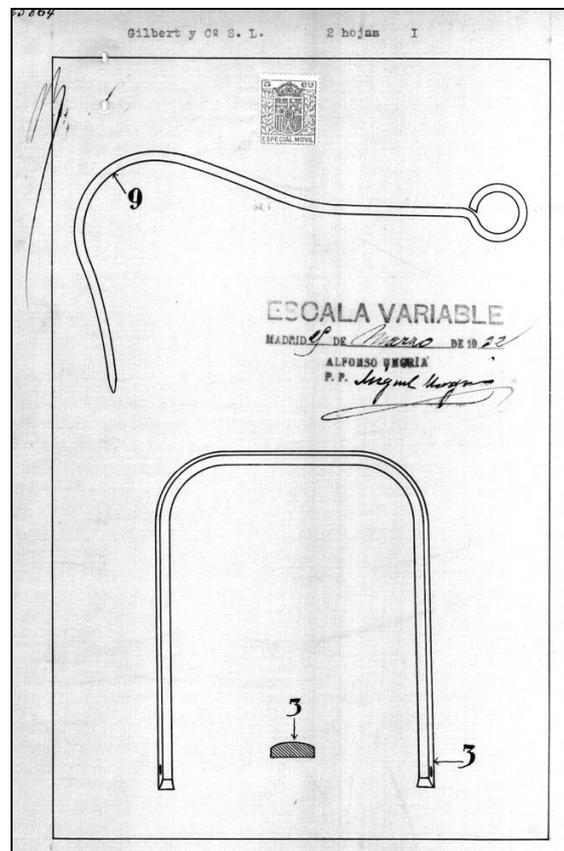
Patente nº 125864. Detalle de asa y gancho (Arch. J.M. Sanchis)
